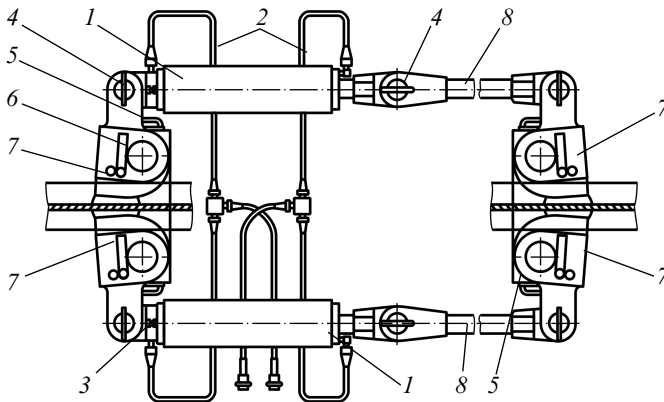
Натяжитель УНГ-75 (вид сверху):
